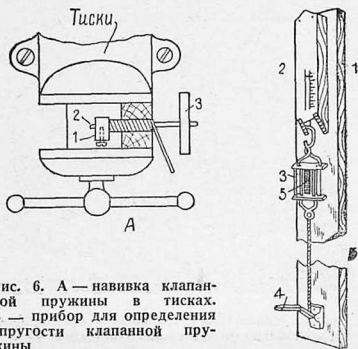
А — навивка клапанной пружины в тисках. В — прибор для определения упругости клапанной пружины
